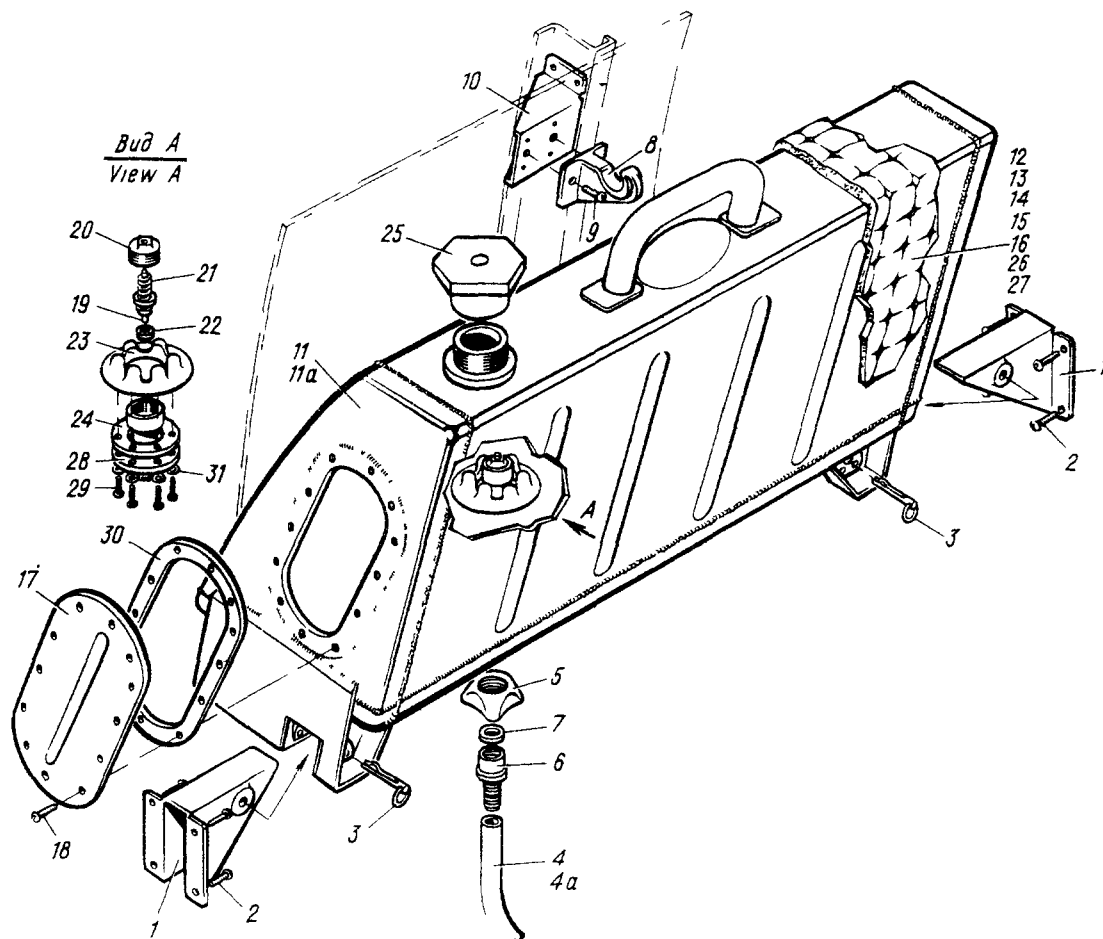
УСТАНОВКА БАКА ДЛЯ ВОДЫ
